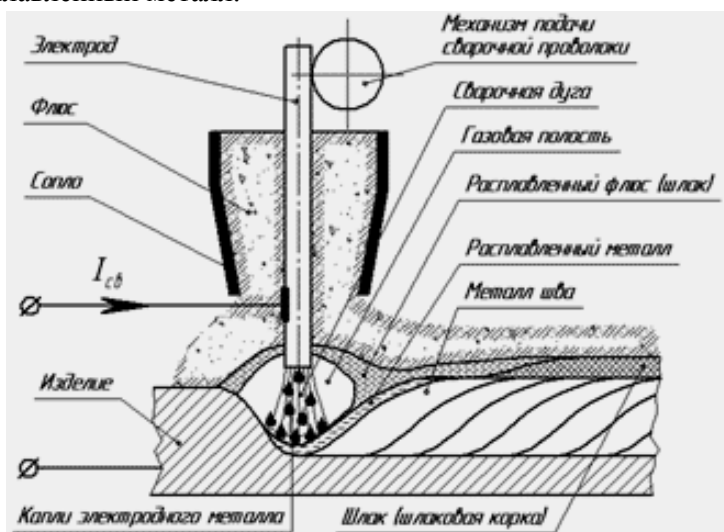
Схема сварки и наплавки под флюсом
